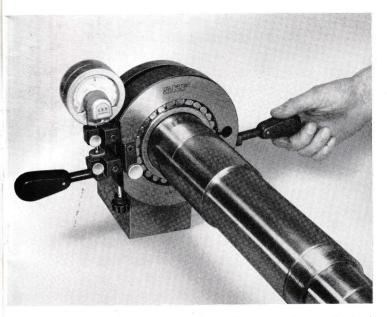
La herramienta de medir según la fig. 1 aplicada al juego de rodillos montados sobre su aro interior
